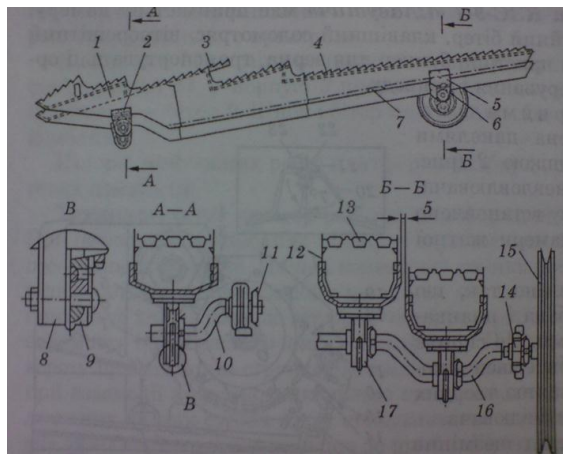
1-клавиша; 2-5-кронштейны; 3-4-гребёнки; 6-прокладка; 7-днище; 8-корпус подшипника; 9- амортизатор; 10- ведомый коленчатый вал; 11-гайка; 12-корпус клавиши; 13-решоточная поверхность клавиши; 14-17-подшипники; 15-шкив; 16-ведущий коленчатый вал.
